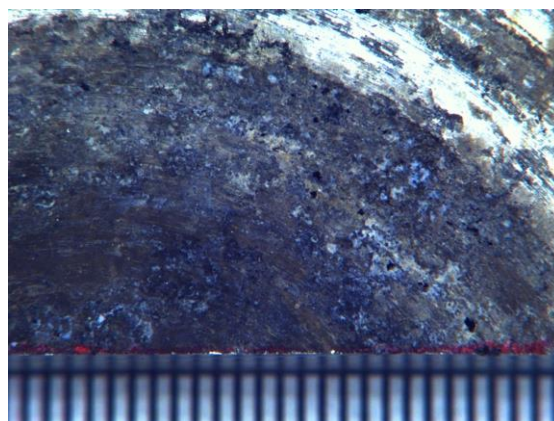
Detalle de la corrosión por picadura de la carcasa superior.
